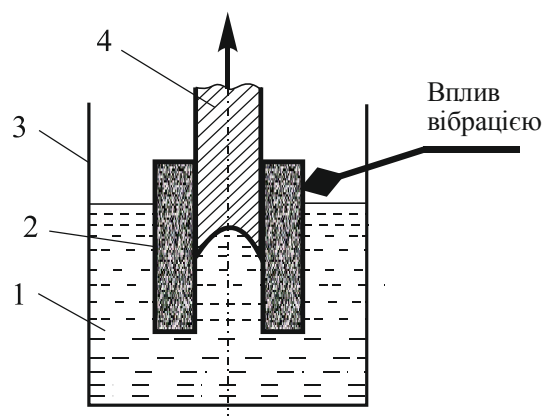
Схема установки датчика коливань при литті мідних заготовок
